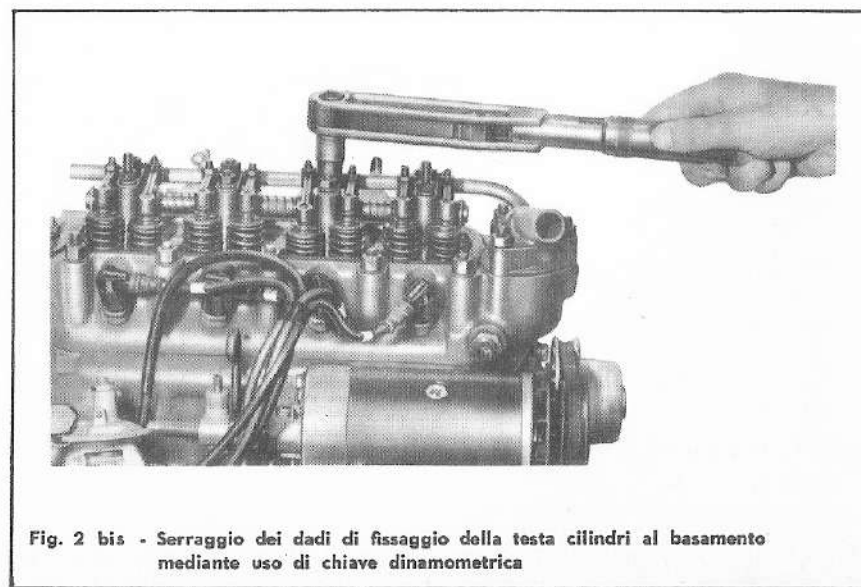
bis - Serraggio dei dadi di fissaggio della testa cilindri al basamento mediante uso di chiave dinamometrica
